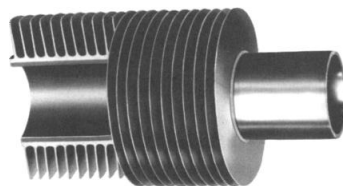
Representação de um tubo com alhetas (alhetas dispostas perpendicularmente ao tubo)²¹
